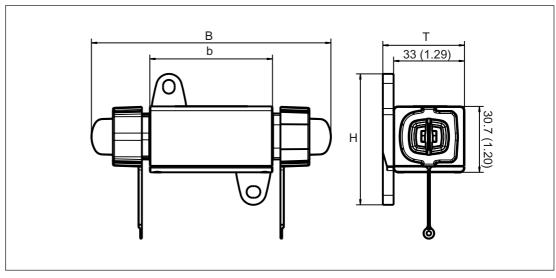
Disegno quotato DRIVE-CLiQ Coupling
